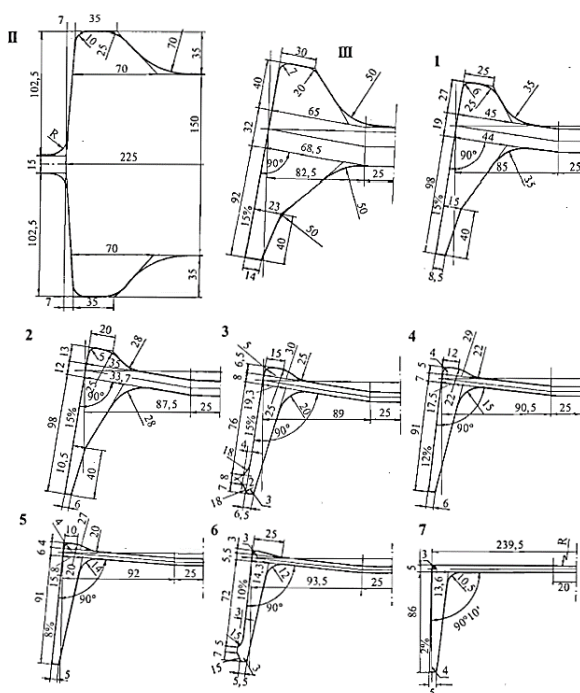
Калибровка швеллера № 24 на рельсобалочном стане Нижнетагильского металлургического комбината [18, с. 40]
